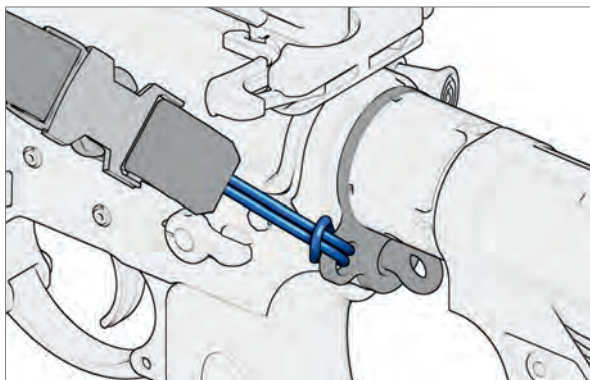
Trageriemen mit Schnellverschluss einschlaufen
